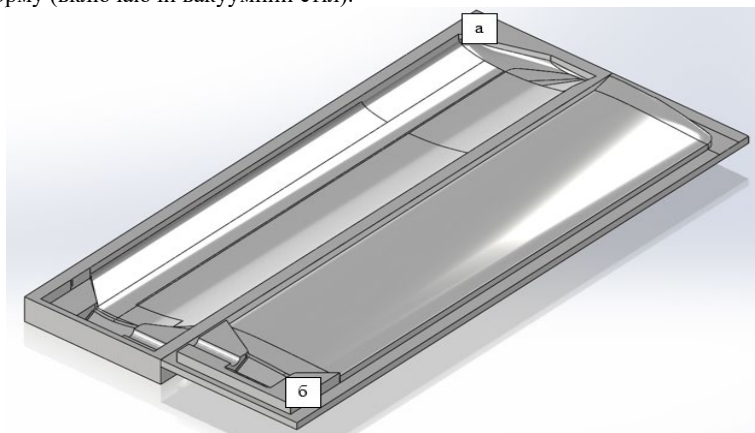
Матриця (а) та пуансон (б) форми для виготовлення лопаті.
